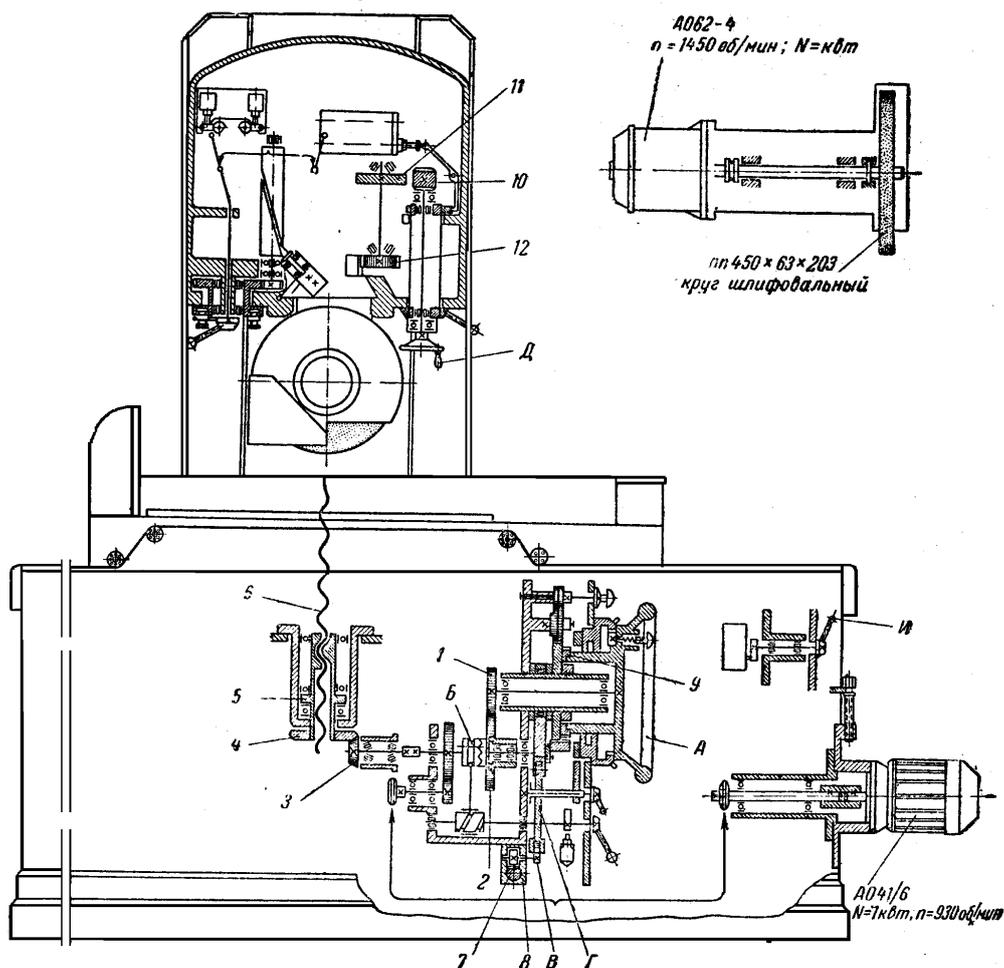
Кинематическая схема универсального плоскошлифовального станка модели 3Б722
